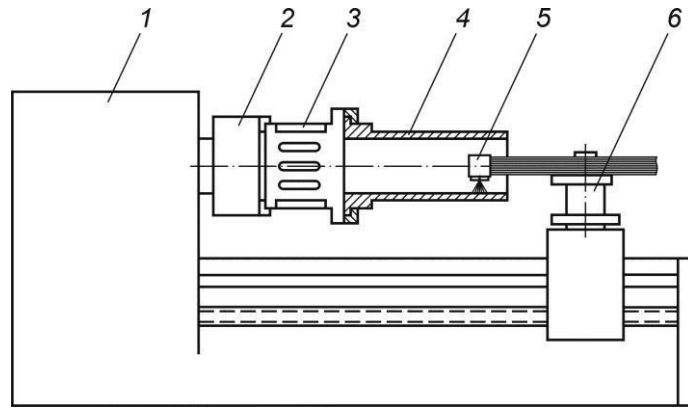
Схема плазмового наплення внутрішньої поверхні гільзи циліндра
